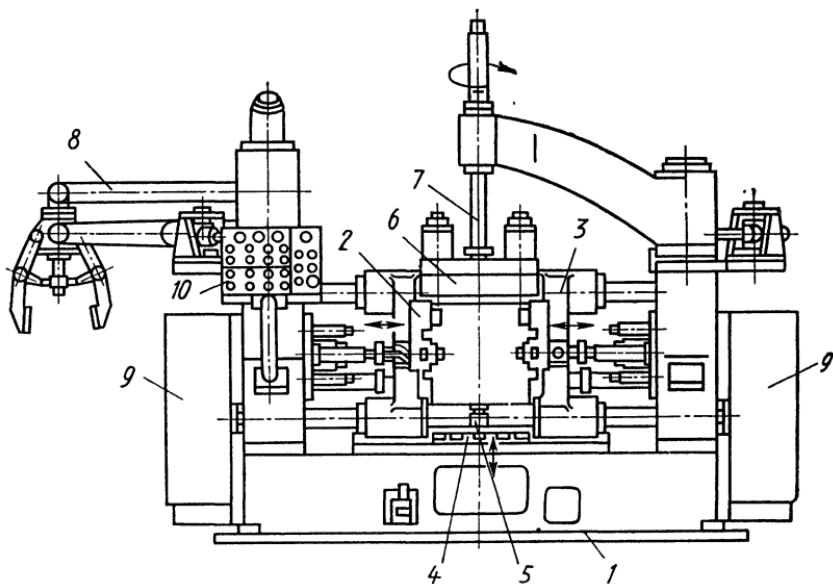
Кокильная машина для отливки сложных по форме деталей
